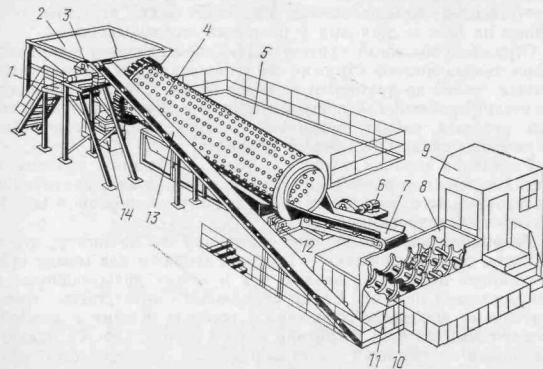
Стружкодробильный агрегат УДСВ-12
